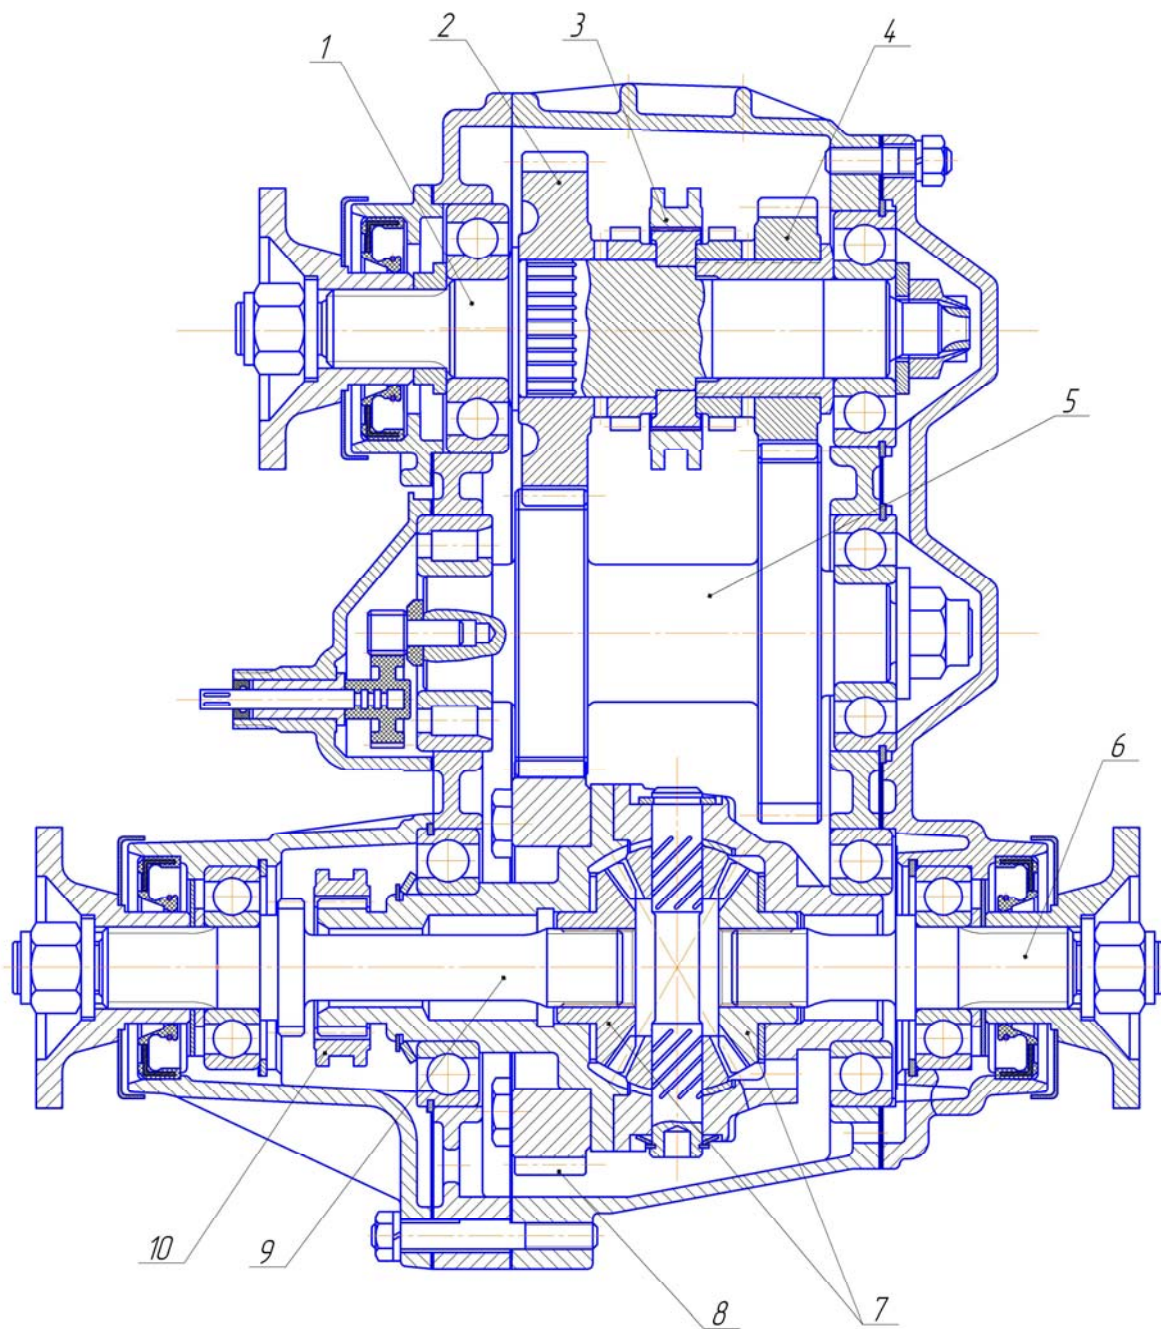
Раздаточная коробка автомобиля ВАЗ-2121
